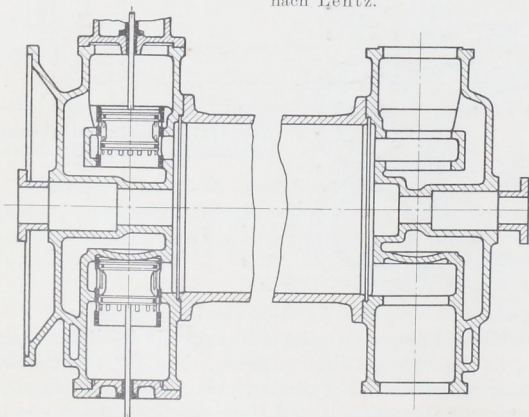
Zylinder mit Kolbenventilsteuerung.
